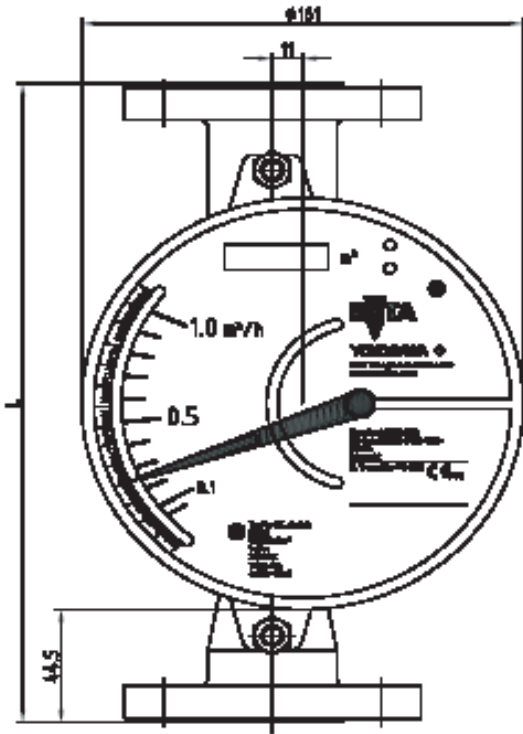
RAMC, вид спереди. Корпус типа 90
